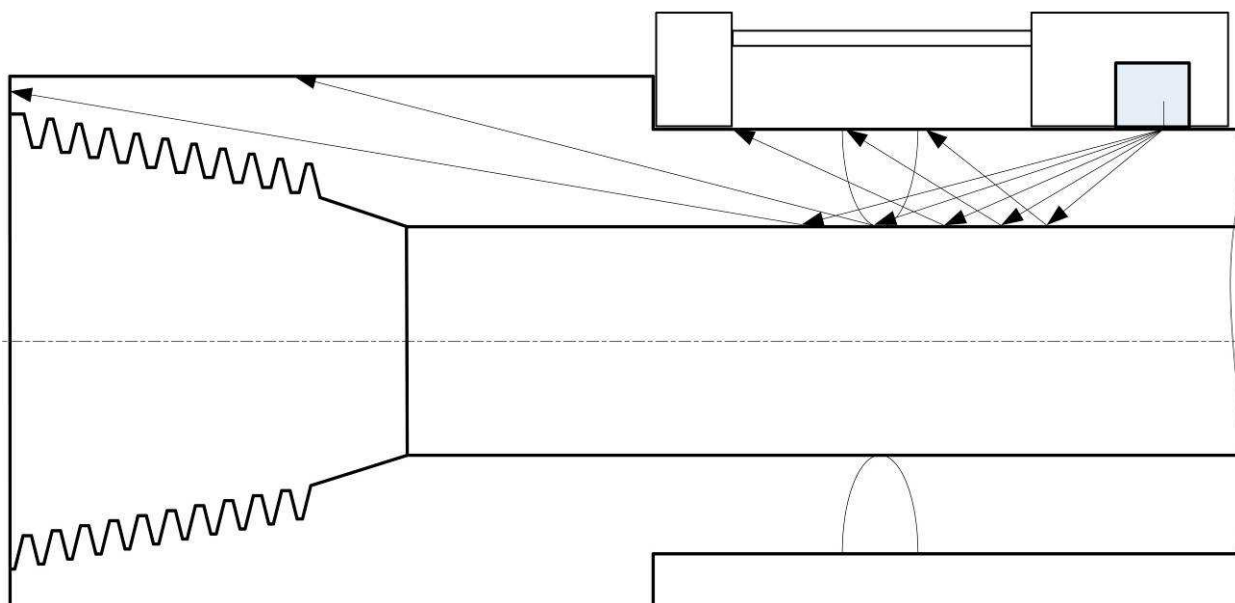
Схема УЗК кольцевого сварного шва бурильной трубы.
